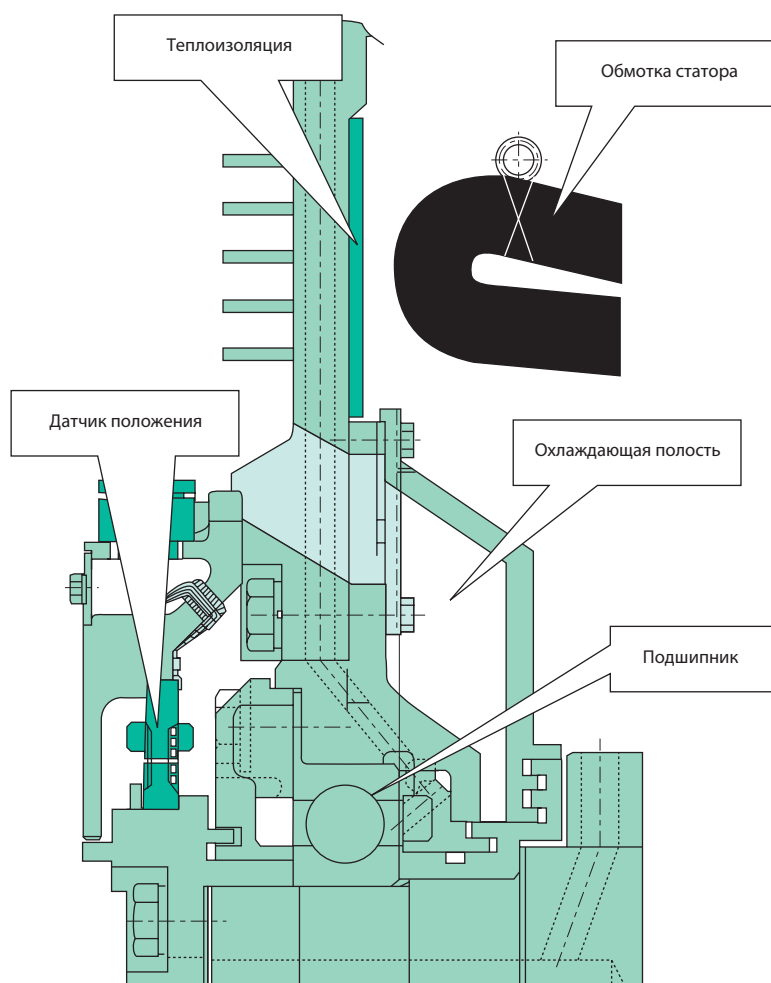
Конструкция подшипникового узла со стороны, противоположной тяговому редуктору и вентилятору
